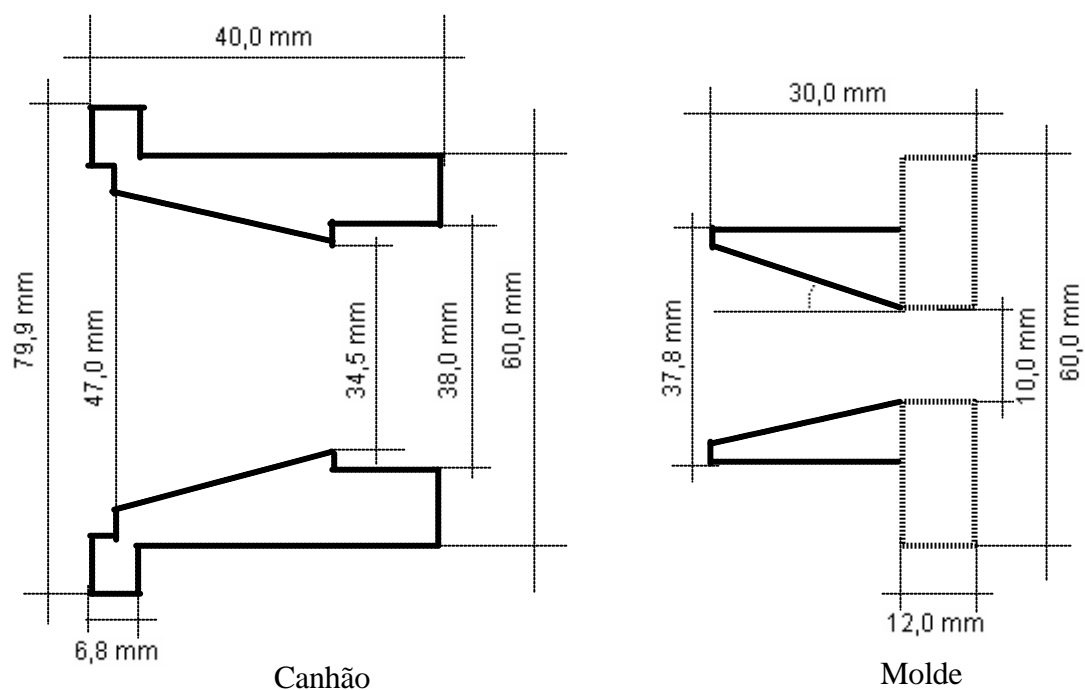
Desenho esquemático do novo conjunto canhão/boquilha da extrusora projetado
